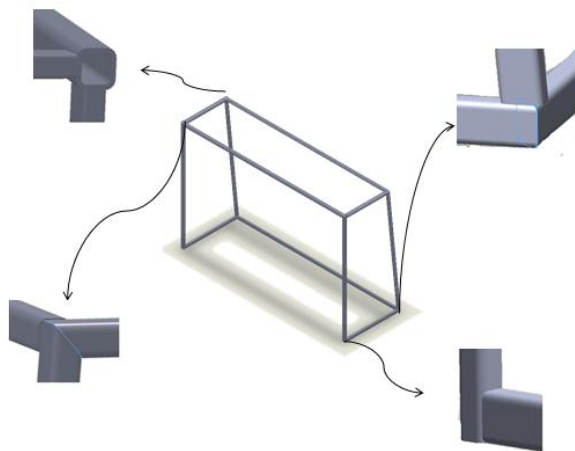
Resumen de la geometría de los nodos en la soldadura
